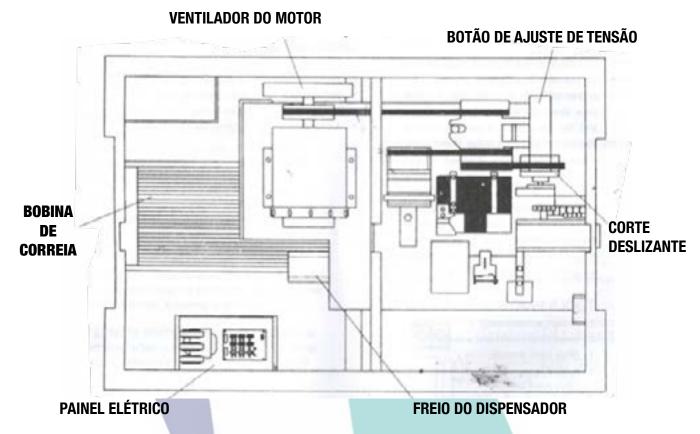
COMPONENTES PRINCIPAIS, VISTA SUPERIOR
